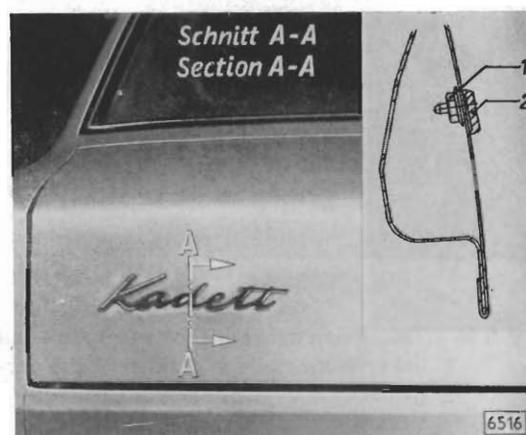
Befestigung des Schriftzuges „Kadett“
